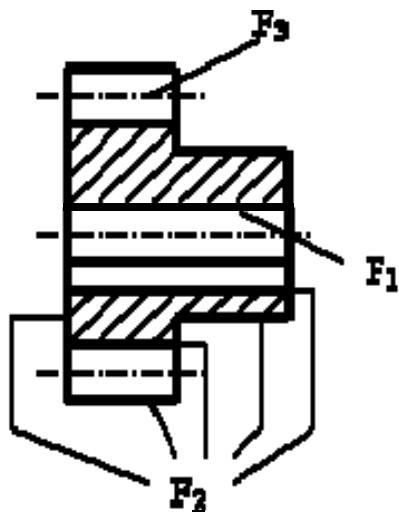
Эскиз детали «Зубчатое колесо»
